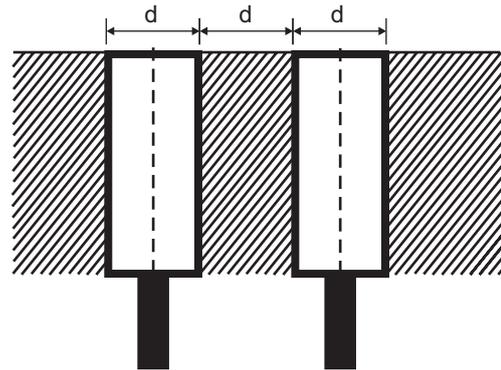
Lange Ausführung, Nicht bündiger Einbau, Steckversion
